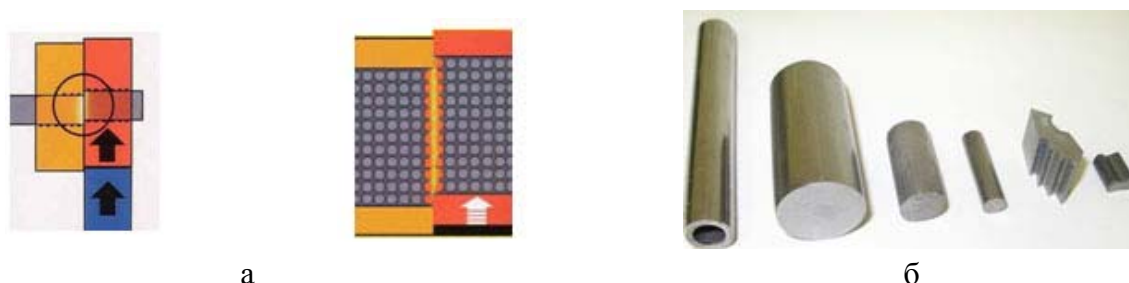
Схема нагружения проката (а) и отрезанные мерные заготовки (б) [9]
